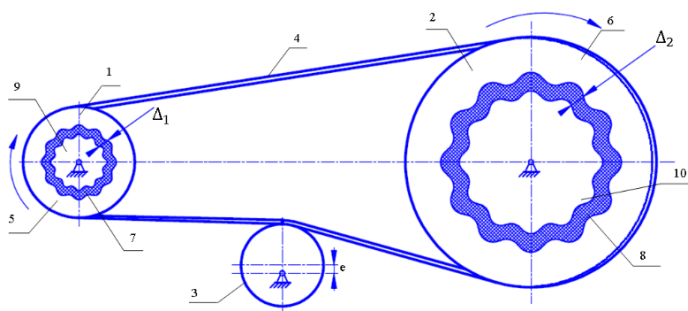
Схема ременной передачи с составными шкивами и эксцентричным натяжным роликом
